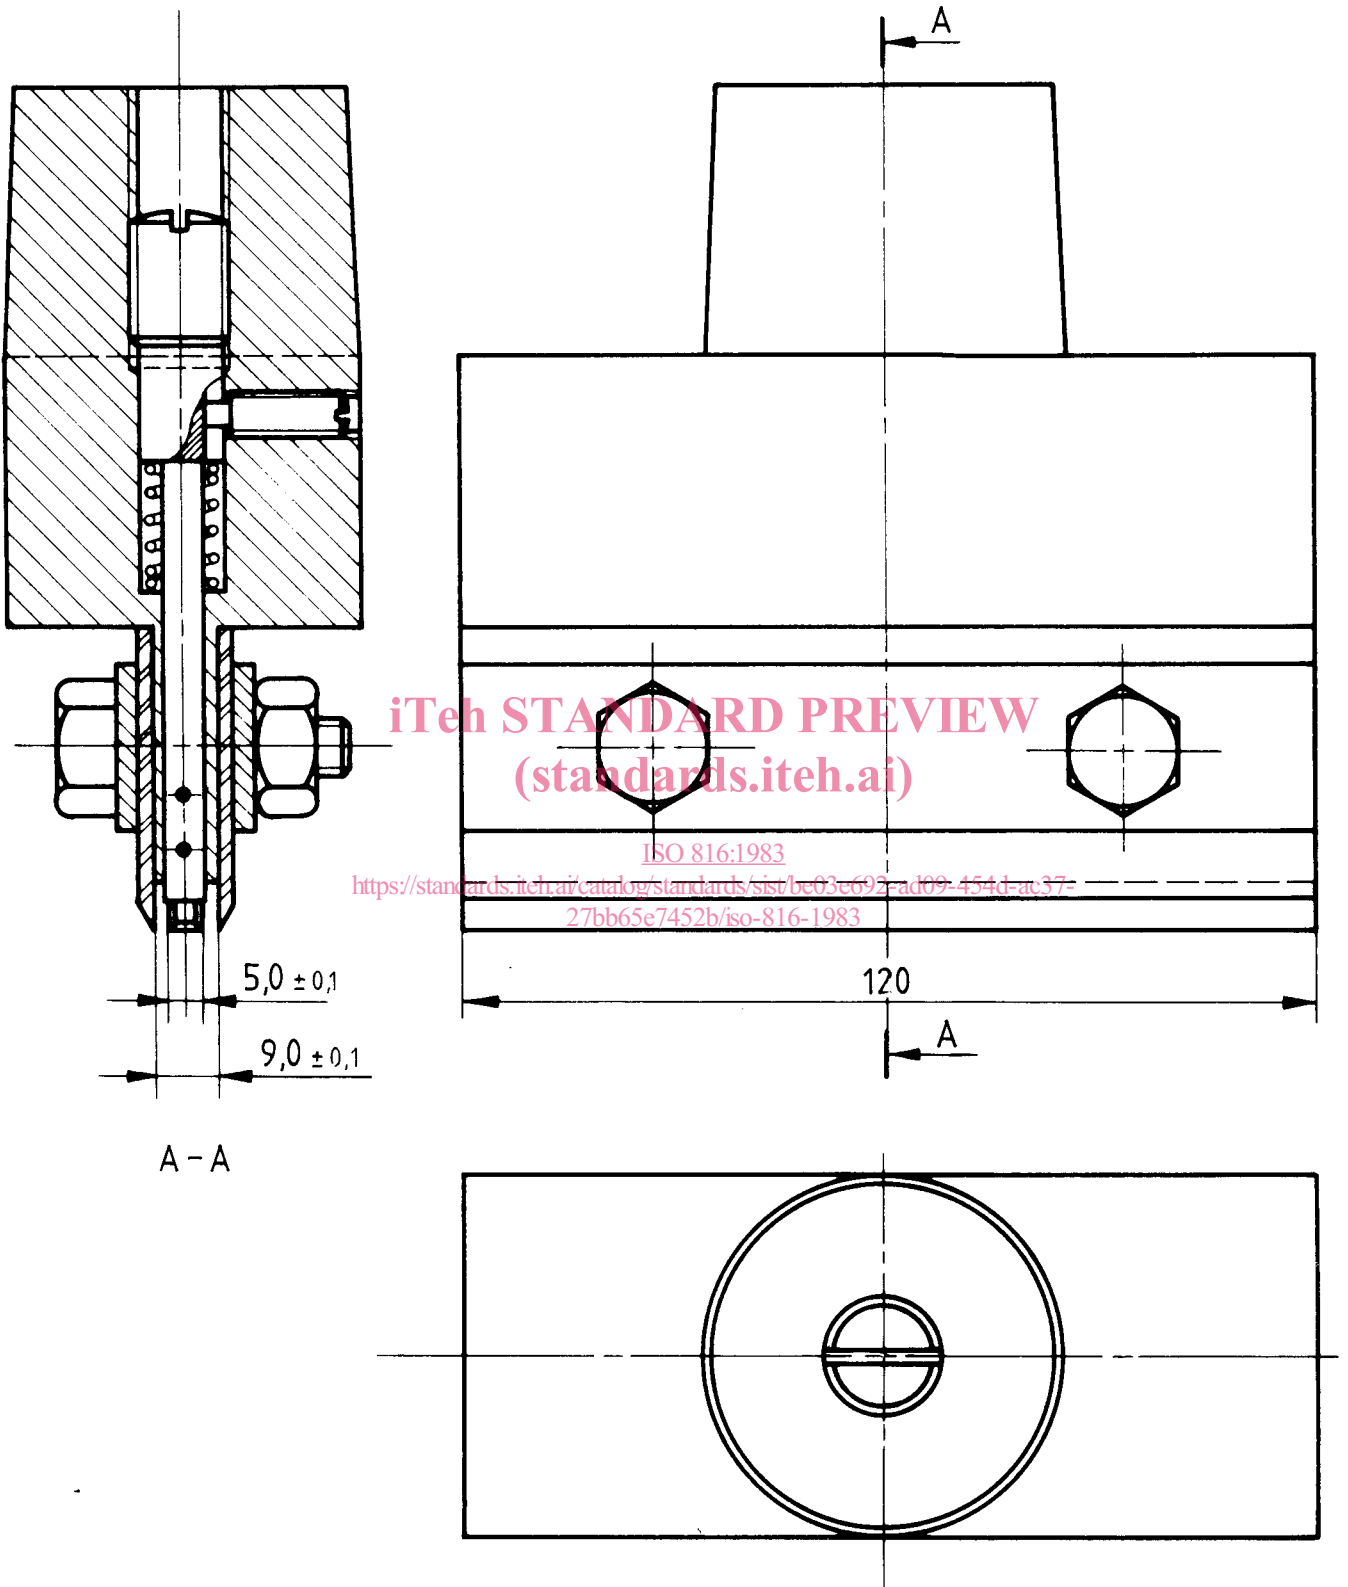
Emporte-pièce pour l'éprouvette de Delft
